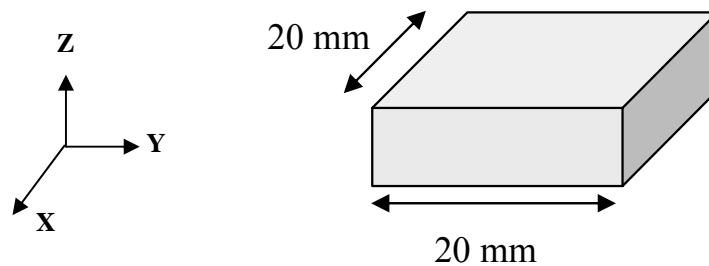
Géométrie des éprouvettes de vieillissement thermique
